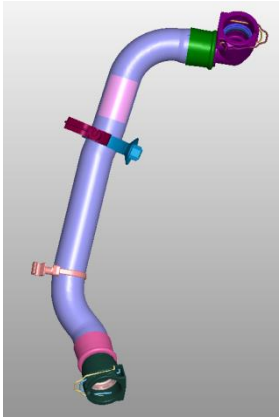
Přípravek pro montáž klipu a stahovací pásy
